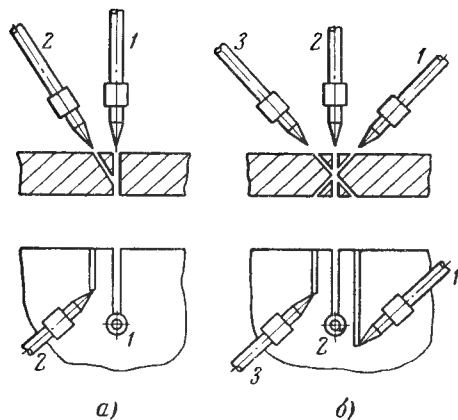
Схема одновременной резки и обработки кромок блоками резачков.
